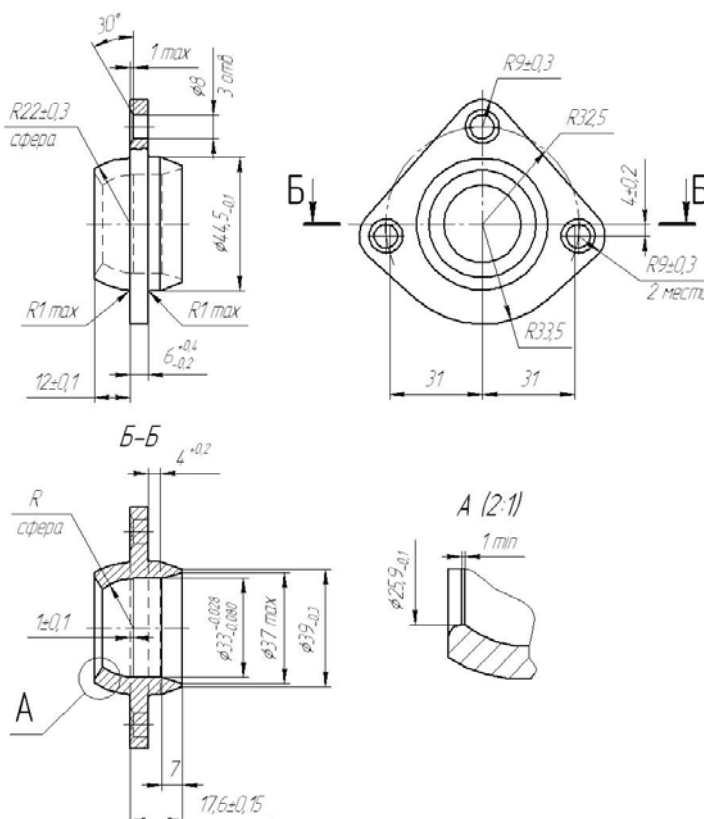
Чертеж штампованной заготовки детали «корпус шарового пальца»
